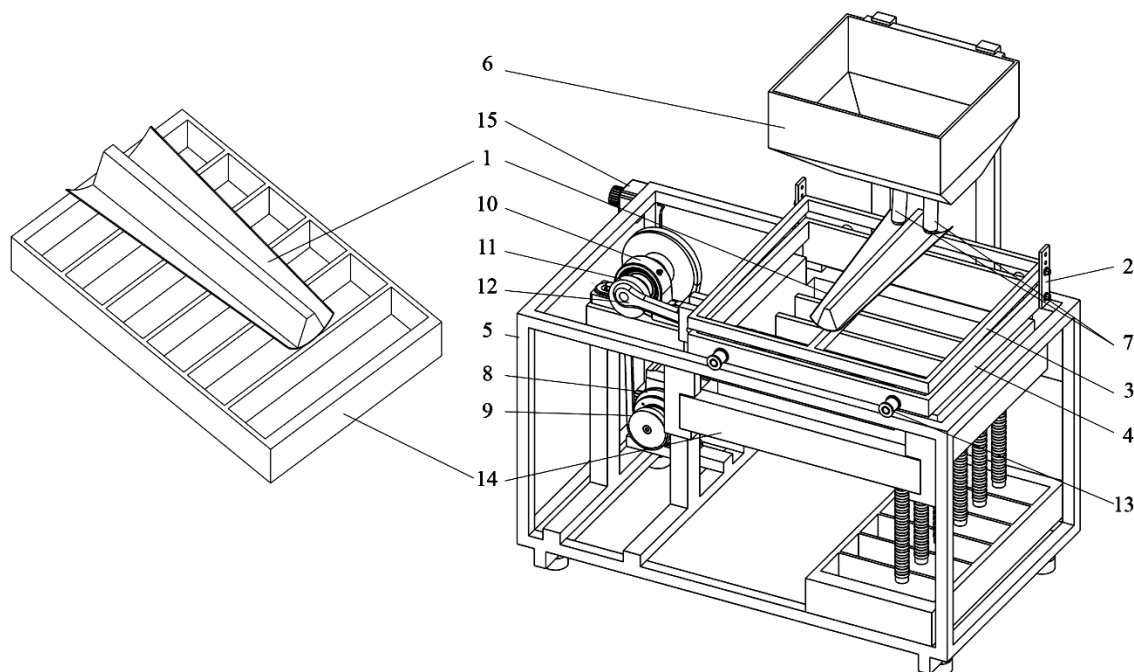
Конструктивная схема сепаратора с одним рабочим органом: 1 – рабочий орган (малогабаритная дека); 2 – механизм регулировки продольного угла наклона; 3 – рама регулировки продольного угла наклона; 4 – вибростол; 5 – станина; 6 – загрузочный бункер; 7 – питающее устройство; 8 – электродвигатель; 9 – клиноременная передача; 10 – промежуточная опора; 11 – механизм регулировки амплитуды колебаний; 12 – шатун привода вибростола; 13 – ролики; 14 – приемники продуктов разделения; 15 – пульт управления.
